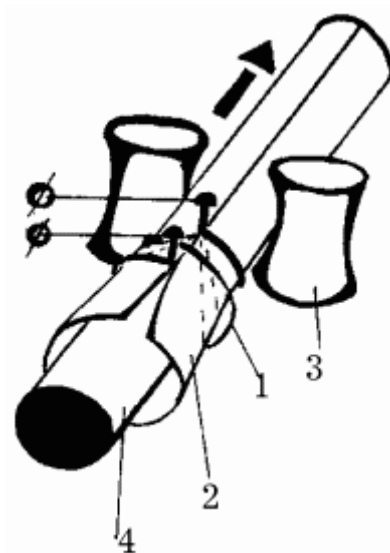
Радиочастотная сварка: 1 – высокочастотный индуктор; 2 – свариваемые части; 3 – ролики; 4 – ферритовый сердечник.
